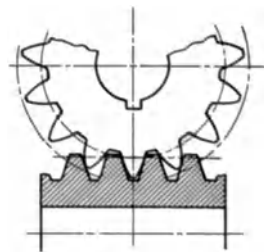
Schneckenrad mit korrigierter Zahnform.
